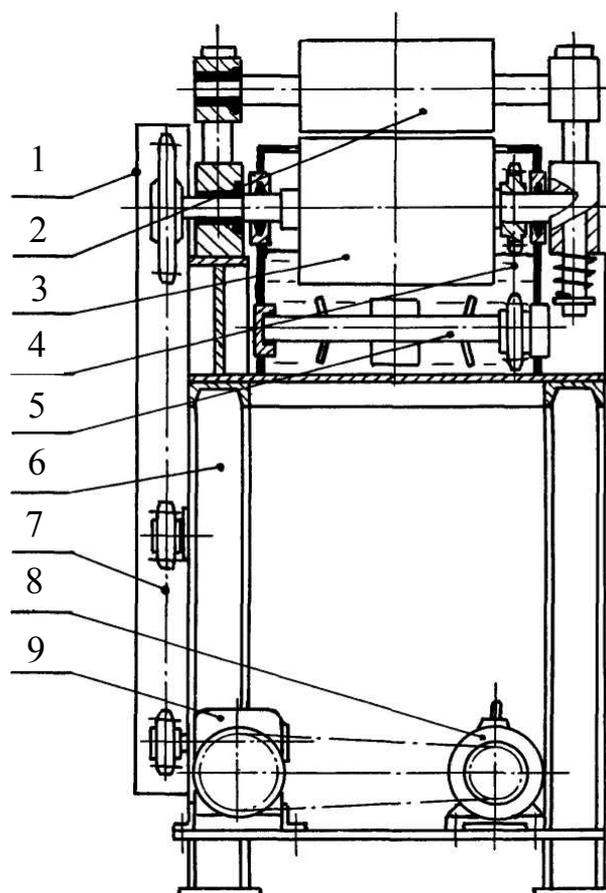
Стенд для нанесения противопопригарного покрытия: 1 – кожух; 2 – прижимной валок; 3 – ведущий валок; 4 и 7 – цепные передачи; 5 – вал-рыхлитель; 6 – станина; 8 – электродвигатель; 9 – редуктор
